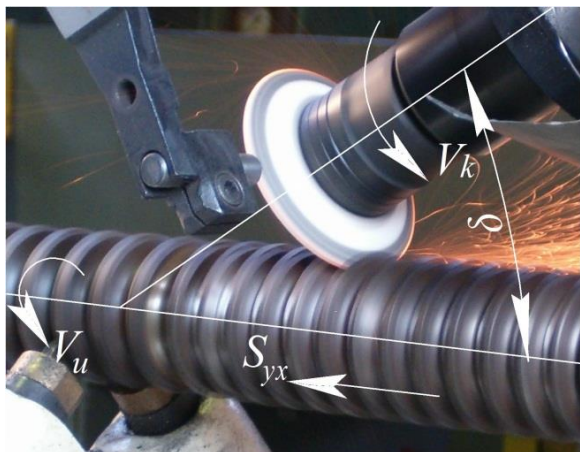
Схема заточки круглой протяжки по передней поверхности зуба
